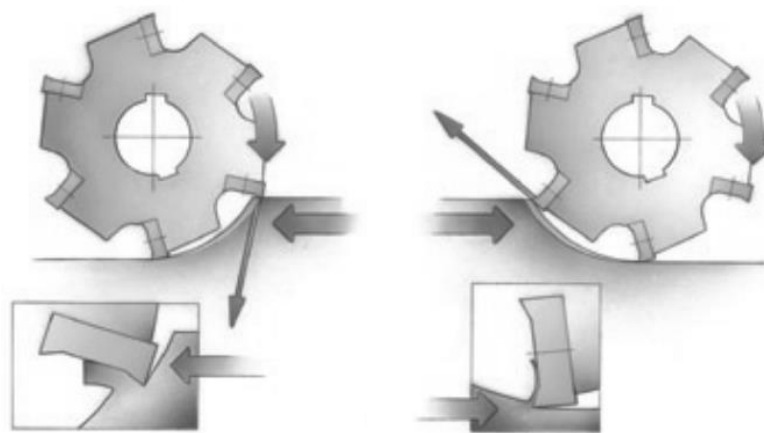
Схеми супутнього і зустрічного фрезерування
